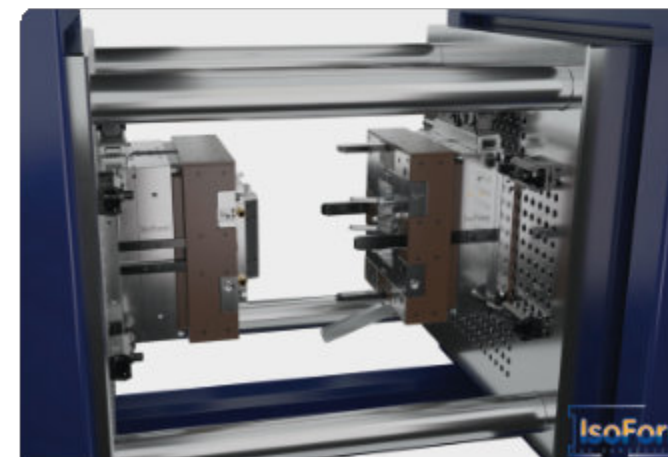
IsoForm®-Wechselwerkzeug auf Maschine
